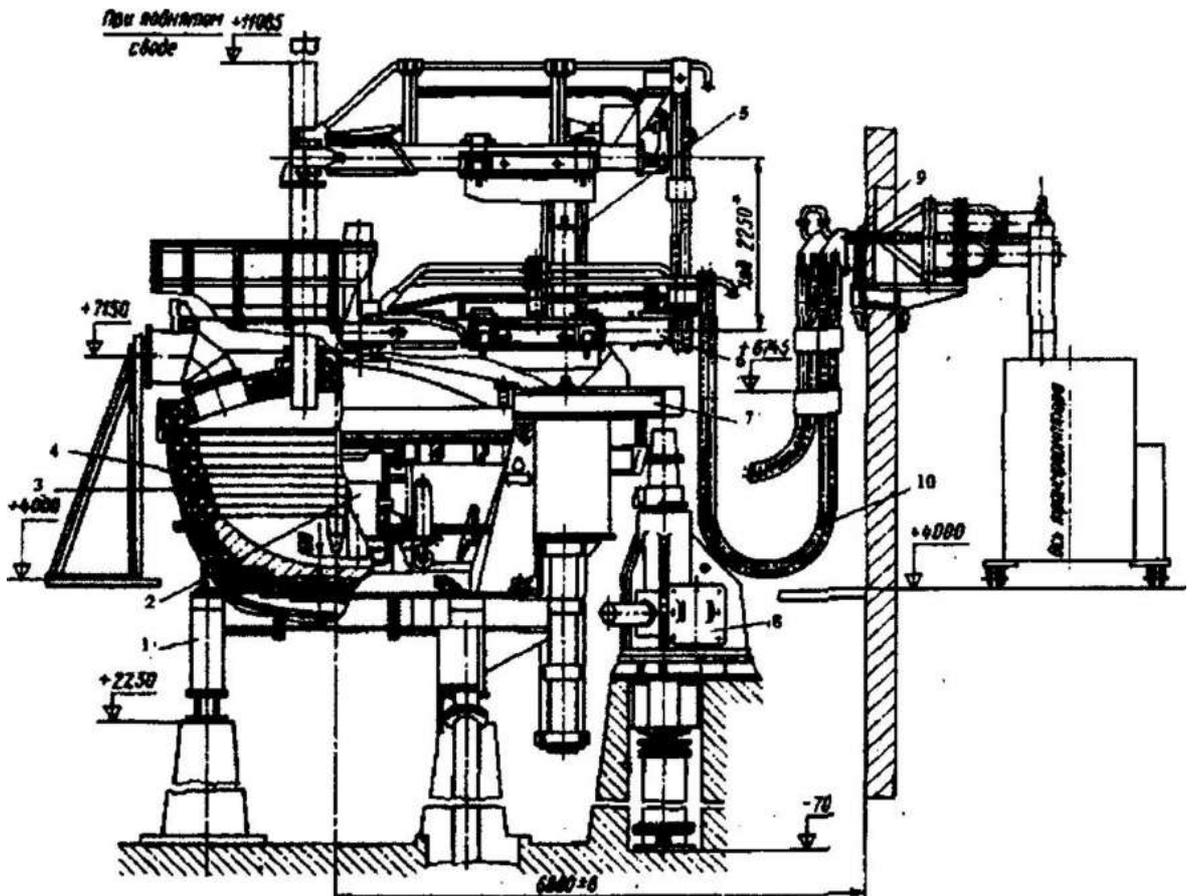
Конструкция дуговой печи ДСП – 3
